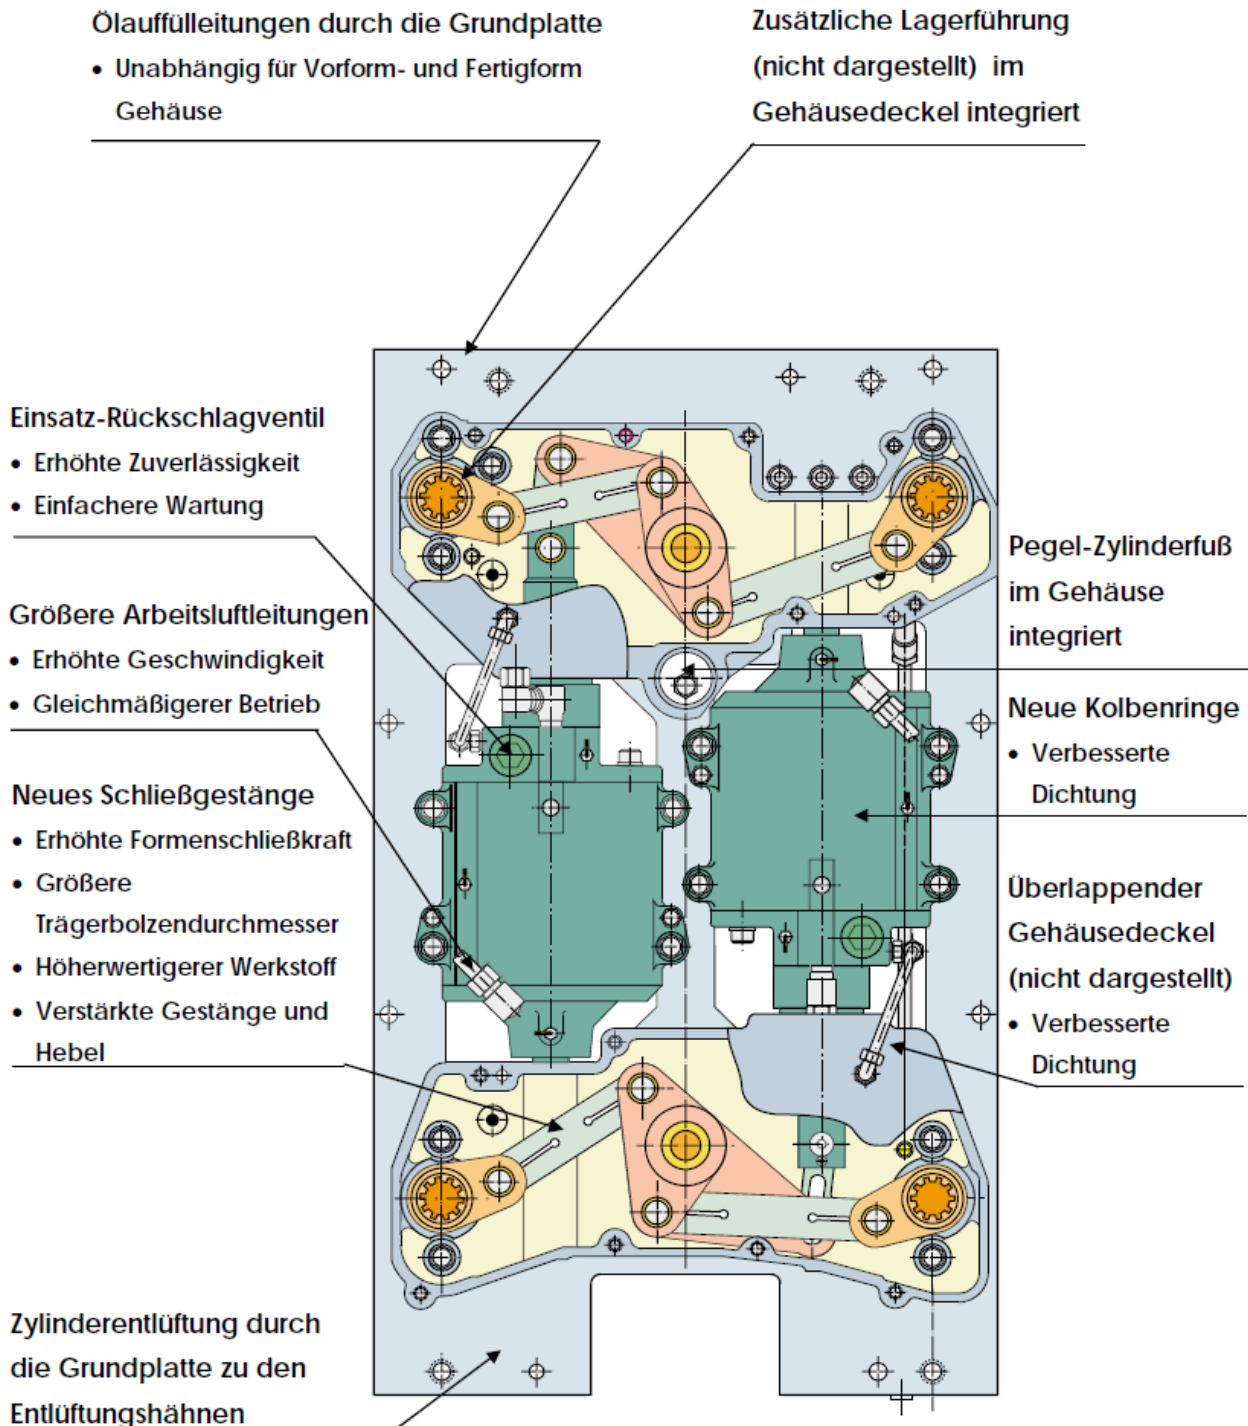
Formenschließmechanismus mit Schließgestänge im Ölbad
